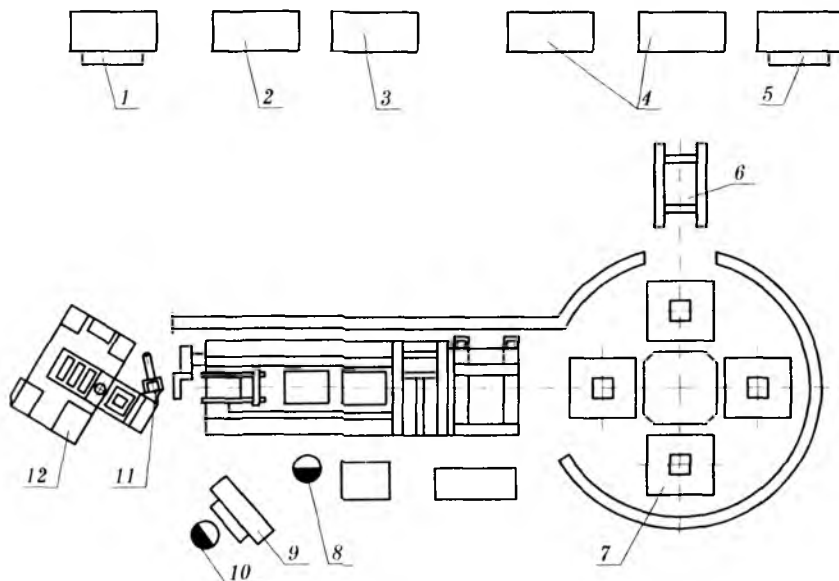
Схема автоматизированной линии по изготовлению оболочковых форм:
